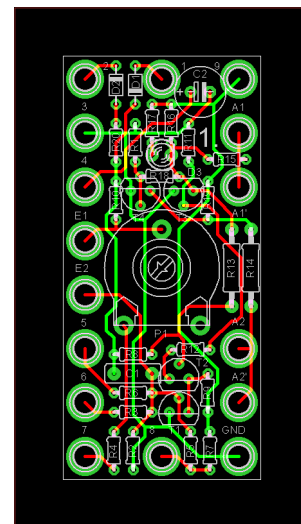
Nachbau 4: Platinenentwurf für das Batteriefach [32263](#)
